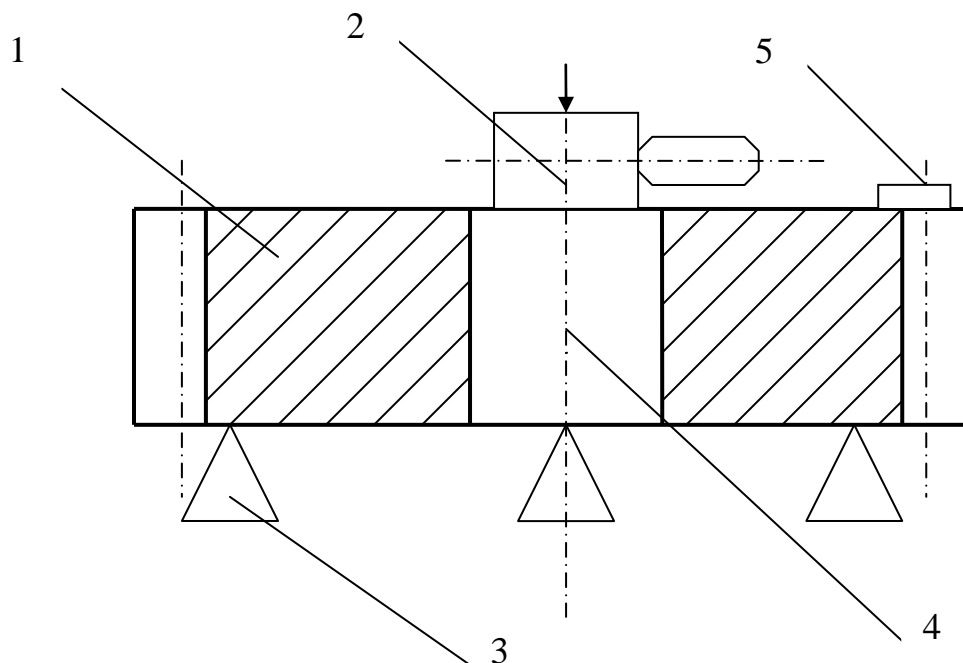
Схема установки крупногабаритного зубчатого колеса
